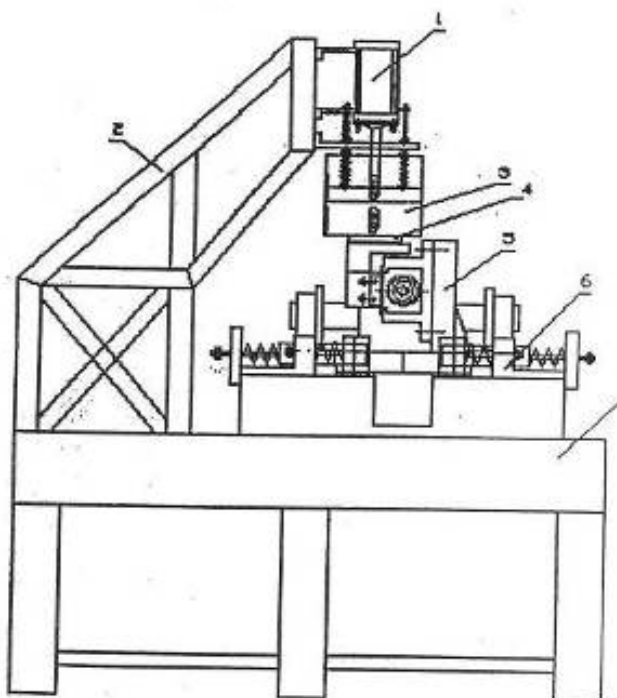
Широкоуниверсальный автоматический самопереналаживающийся сборочный центр.
